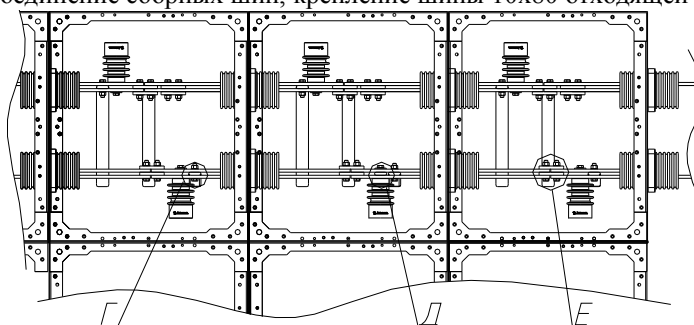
Монтаж сборных шин 1600 А (вид сверху на шкафы КРУ)
